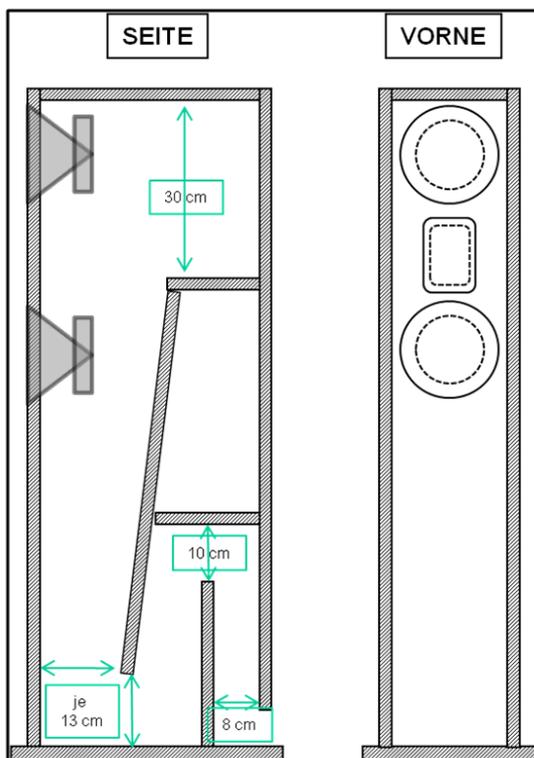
Gehäuseskizze mit minimaler Bemaßung; die restlichen Maße sind in der Gehäuse-Stückliste zu finden
